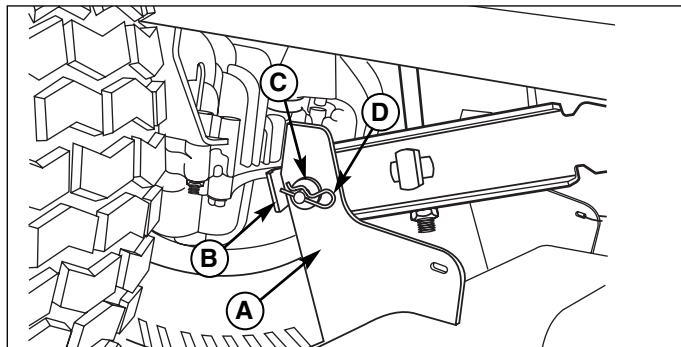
Bracci di sollevamento (vista dal lato destro in basso del trattore)
